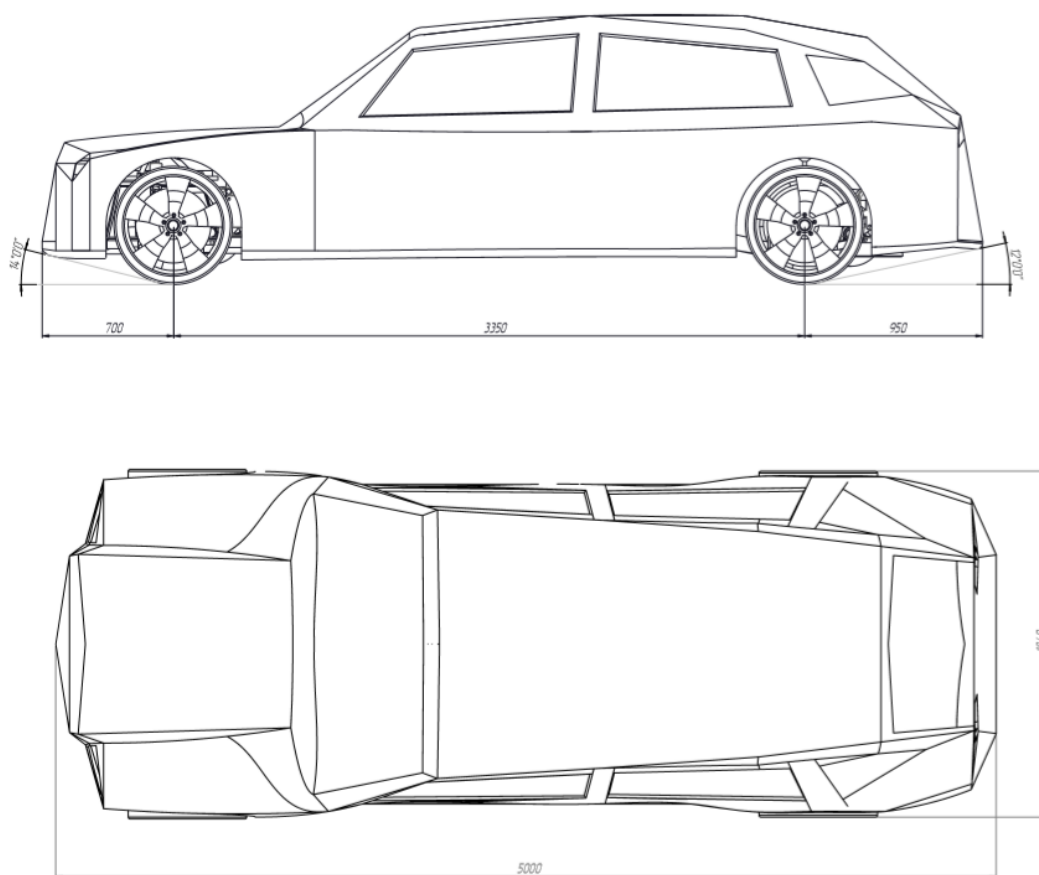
Загальний вигляд електромобіля(Вид збоку та Вид зверху).
